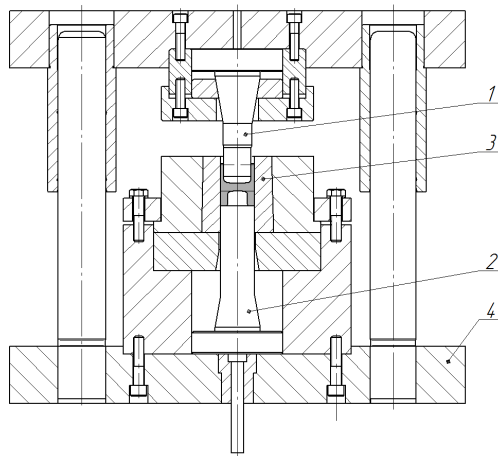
Схема штамп для двостороннього видавлювання з обмеженням течії металу: 1 – верхній пуансон; 2 – нижній пуансон; 3 – контейнер-матриця; 4 – штампний блок з колонками-втулками та виштовхувачем
